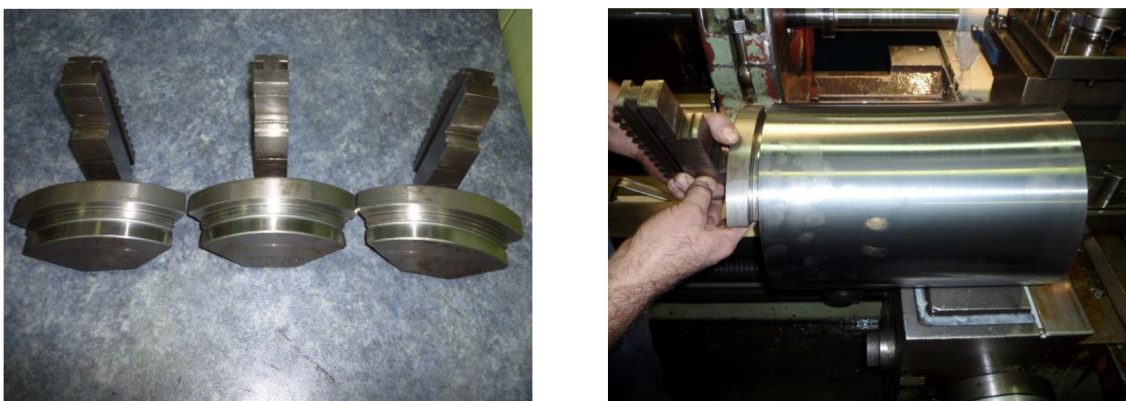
Univerzální hrotový soustruh SU 63.
